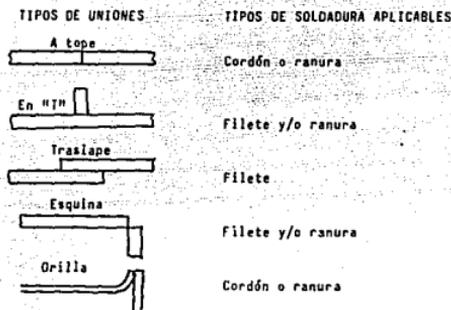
Tipos básicos de uniones con soldadura con fusión, y tipos de soldaduras usados para hacerlos.
